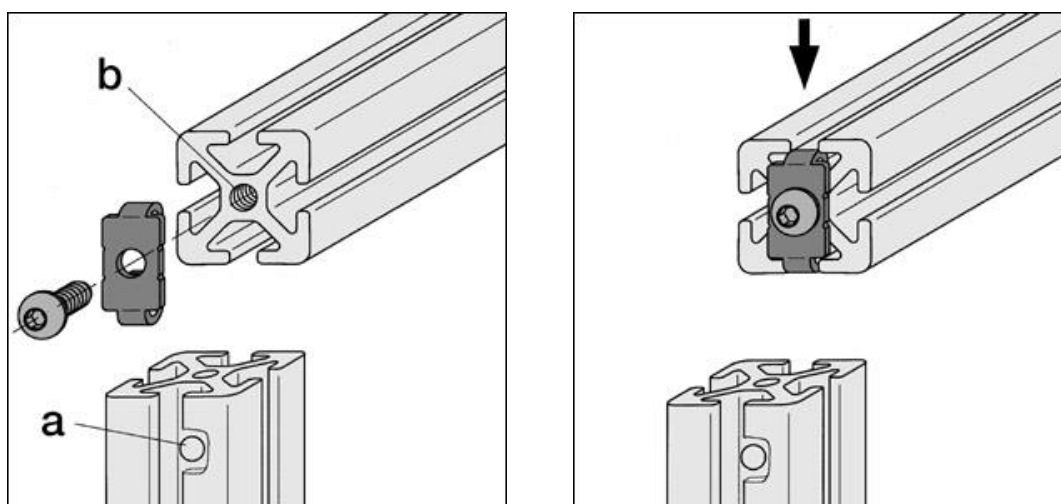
Esquema de ensamblaje de uniones ITEM para estructura
